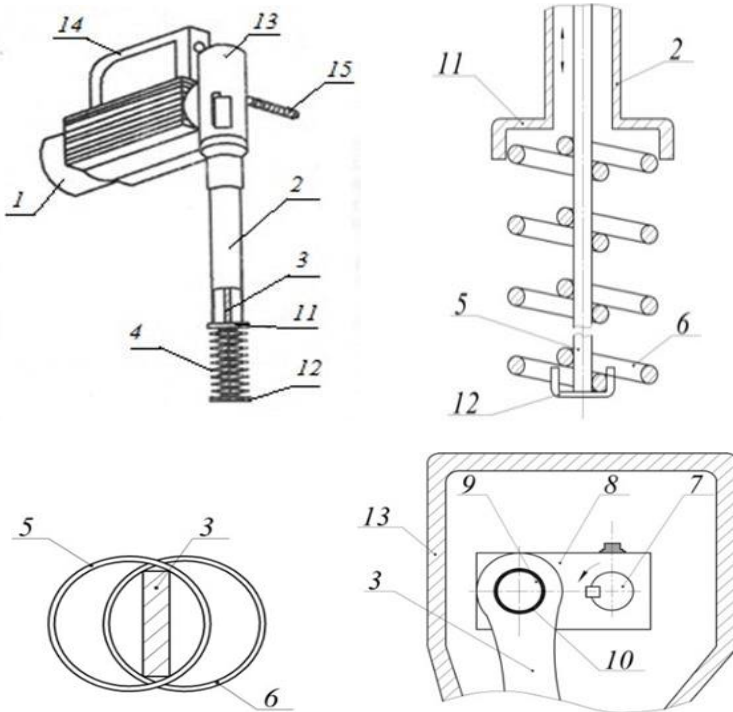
Конструкция пружинного виброуплотнителя с двумя совмещенными виброизлучателями:
